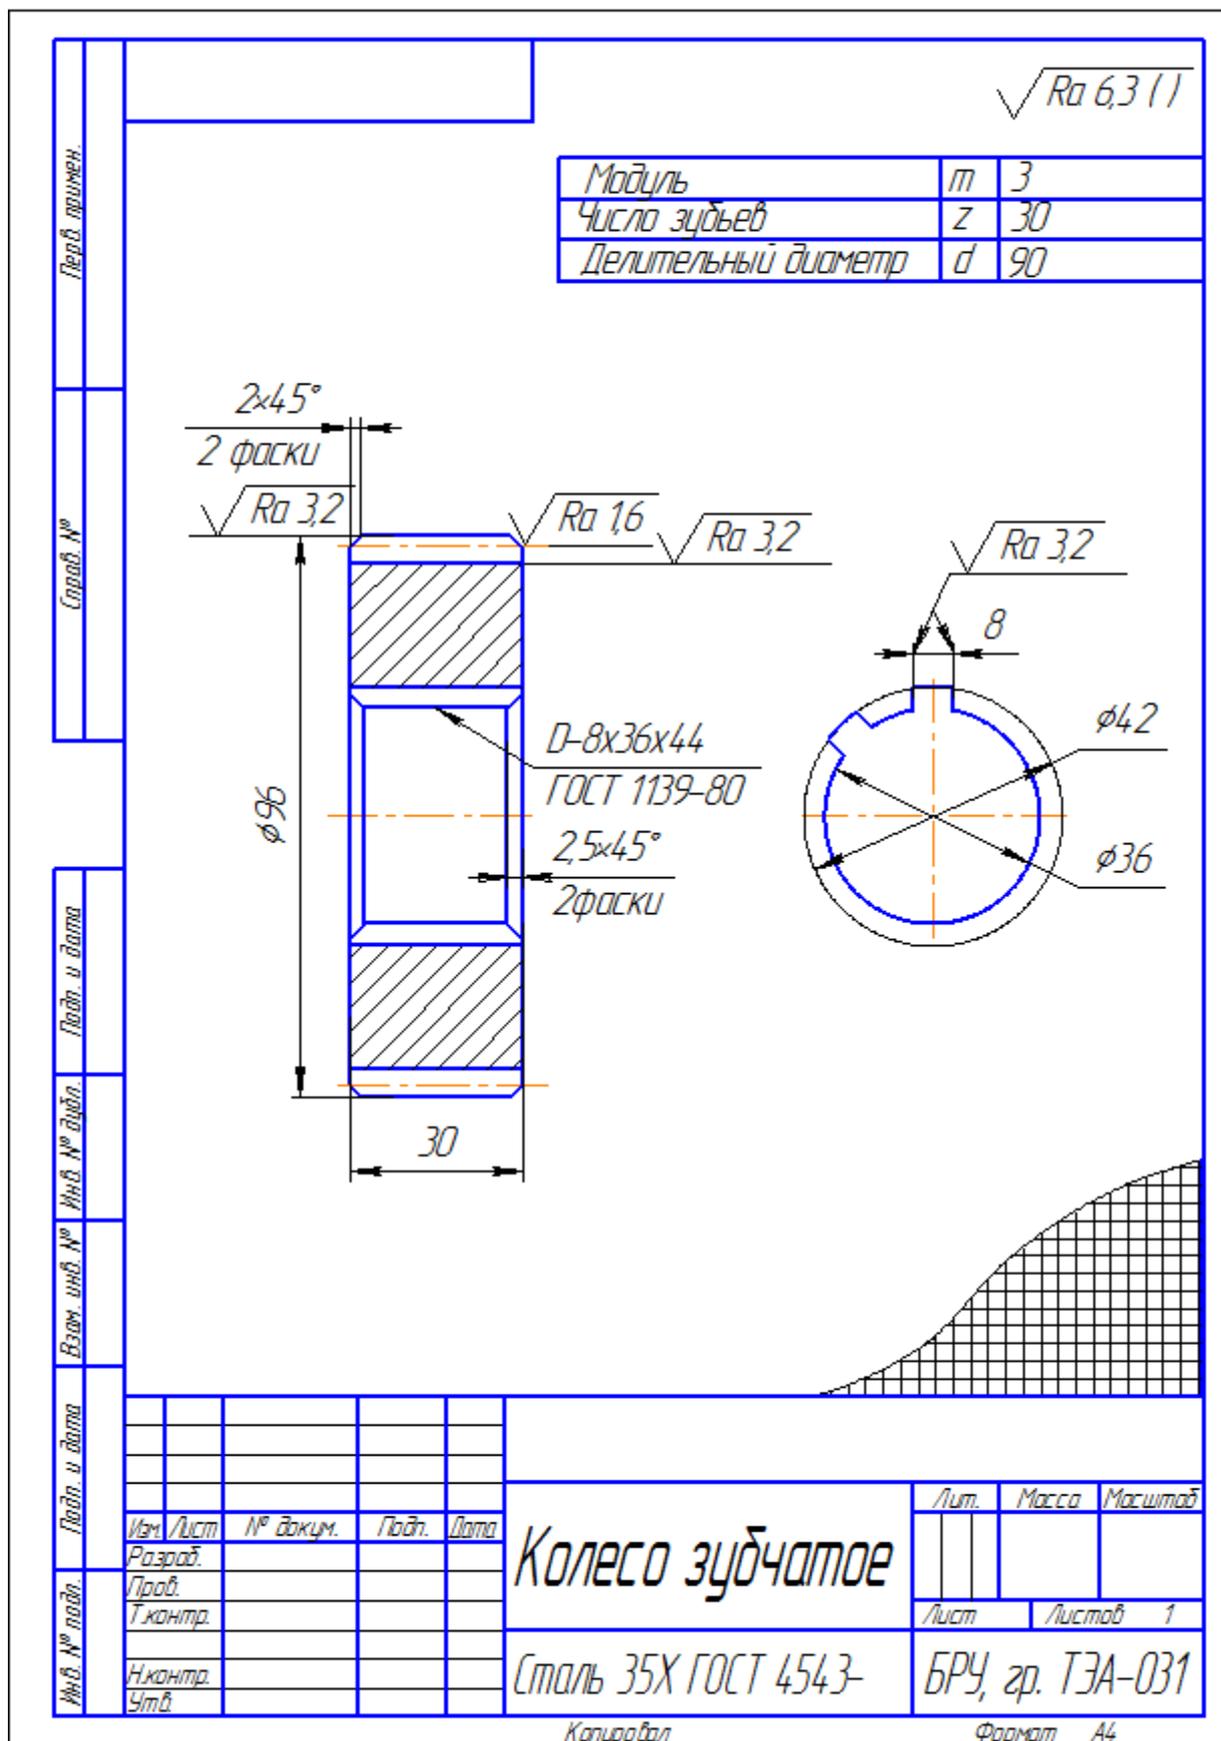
Образец выполнения эскиза колеса зубчатого
